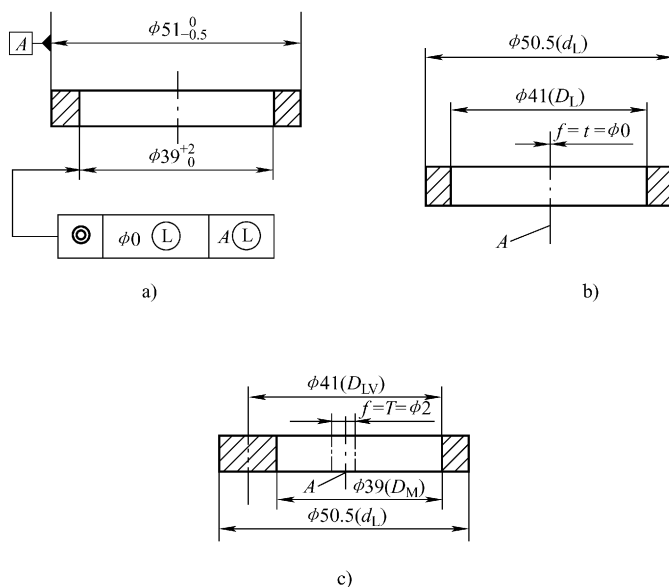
同轴度公差采用最小实体要求的零几何公差
